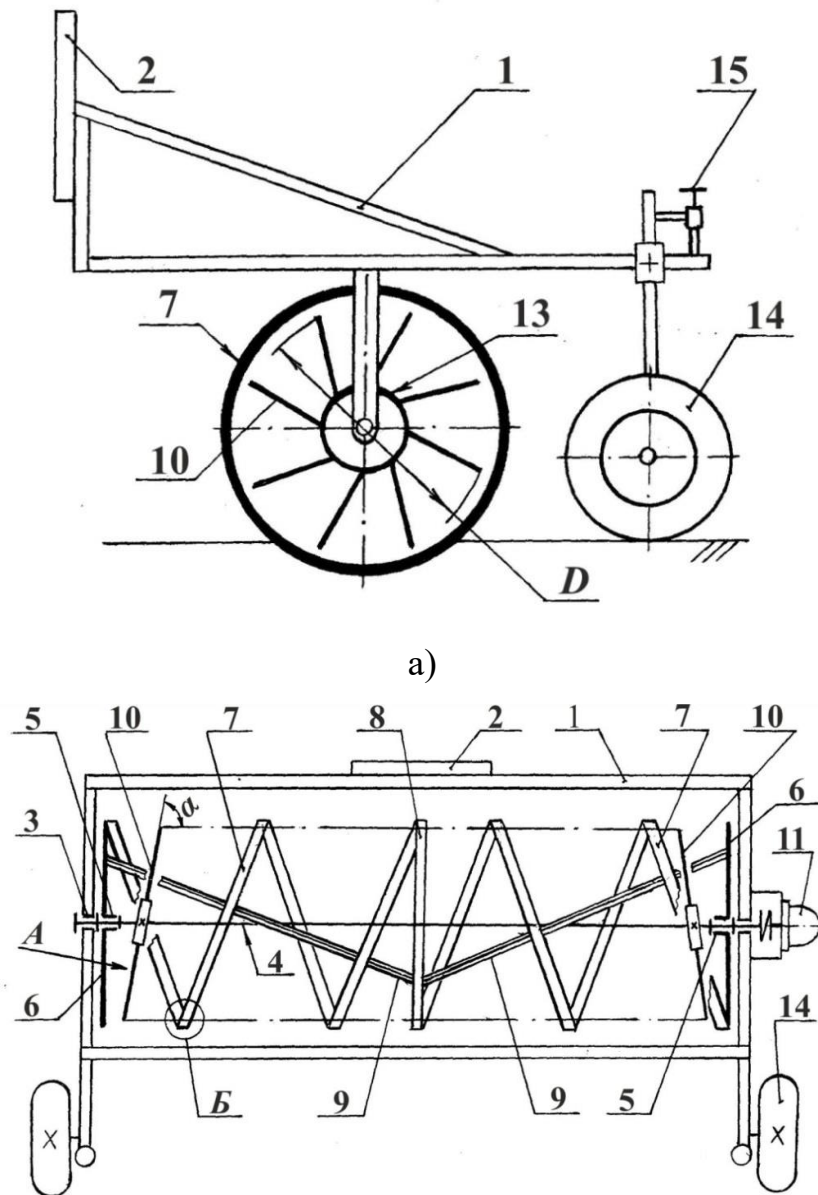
Конструктивно-технологічна схема ротаційного знаряддя (а - робоче положення; б - вигляд зверху): 1 – рама; 2 – механізм навішування; 3 і 5 – підшипникові опори; 4 – вал; 6 – круглі бічні диски; 7 – стрічкові спіралі; 8 – з'єднувальне кільце; 9 – гвинтові квадратні прутки; 10 – еліпсоподібні голчасті диски; 11 – гідромотор; 12 – голка диска; 13 – маточина диска; 14 – опорні колеса; 15 – гвинтовий механізм регулювання глибини обробки [4].
